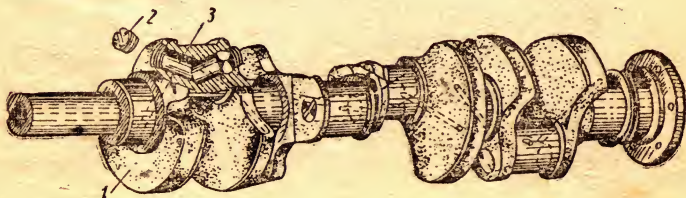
Коленчатый вал двигателя ЗИЛ-130:
